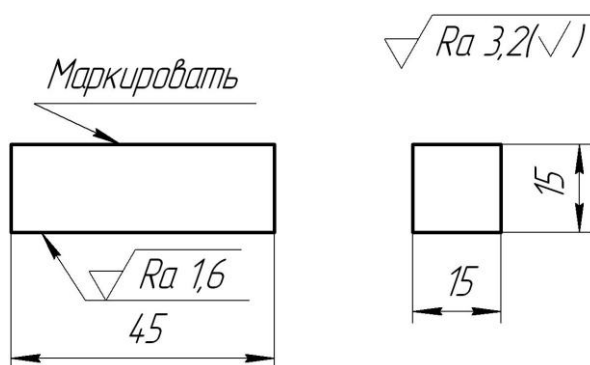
Заготовки из сталей Р6М5 и ШХ15 для шлифования периферией круга
